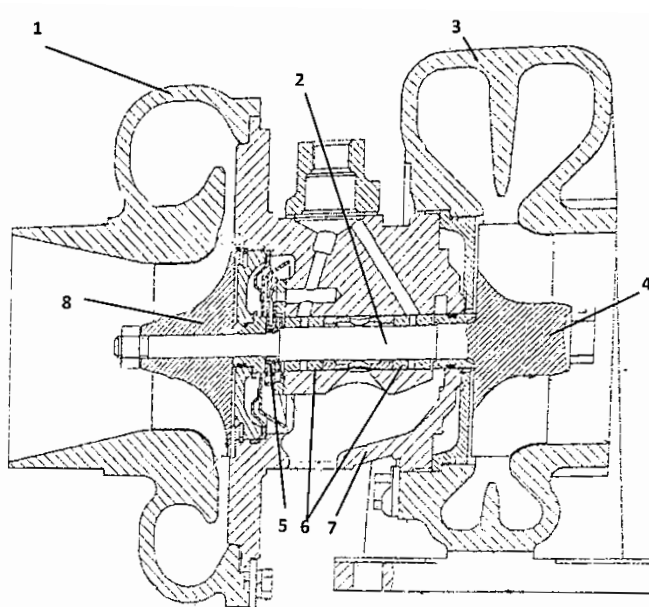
Схема турбокомпрессора: 1 – Корпус компрессора, 2 – Вал ротора, 3 – Корпус турбины, 4 – Колесо турбины, 5 – Уплотнительные кольца, 6 – Подшипники, 7 – Корпус подшипников, 8 – Колесо компрессора.
